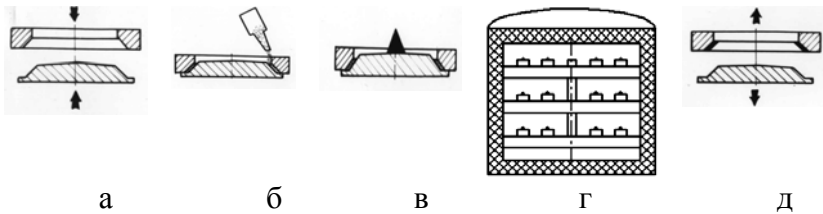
Схема формування плакування: а – установка деталі на технологічну форму; б – заповнення зазору наповнювачем; в – дозування й установлення просочувального сплаву; г – нагрівання у вакуумній печі; д – видалення форми
